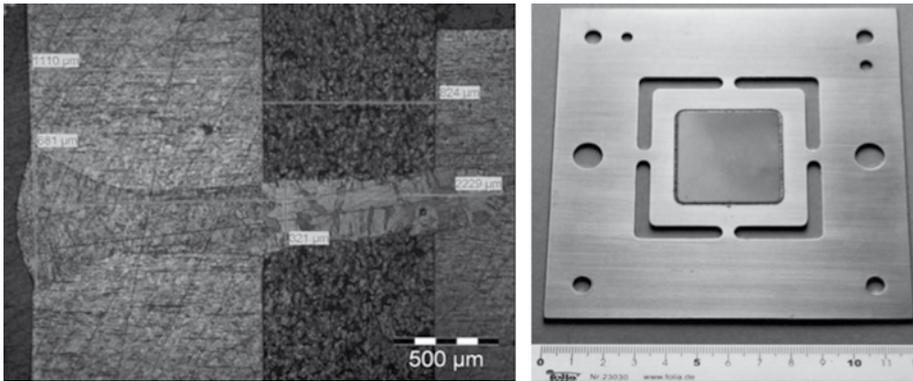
Integration poröser Sintermetallfritten mittels Durchschweißung (links) und Integration einer porösen Sintermetallfritte mit I-Stoß (Crofer 22 APU, 1.4760) (rechts)
